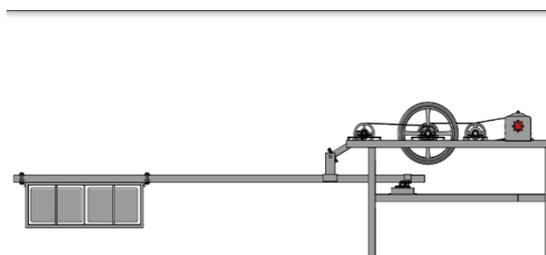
Tampak depan 3D model pembangkit listrik tenaga gelombang laut
